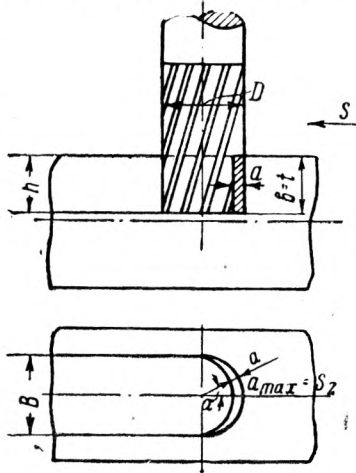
Размеры сечения стружки при фрезеровании паза концевым фрезером
